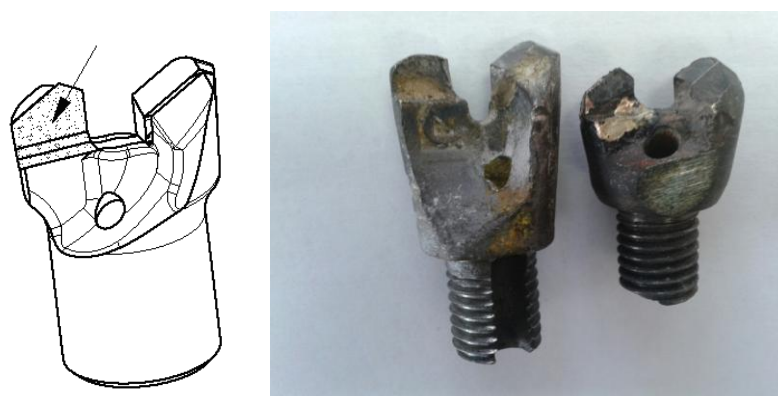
Буровой резец с оторванной режущей пластиной
